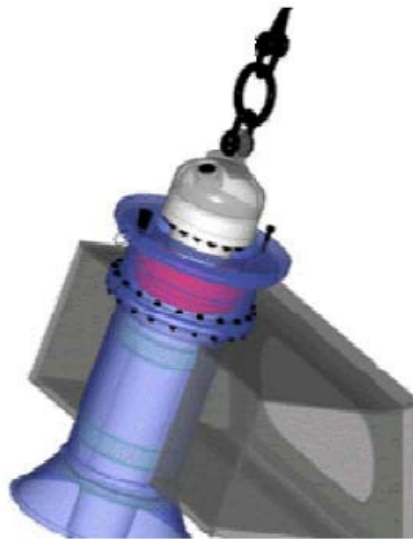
Втяжное устройство для передачи нагрузок
